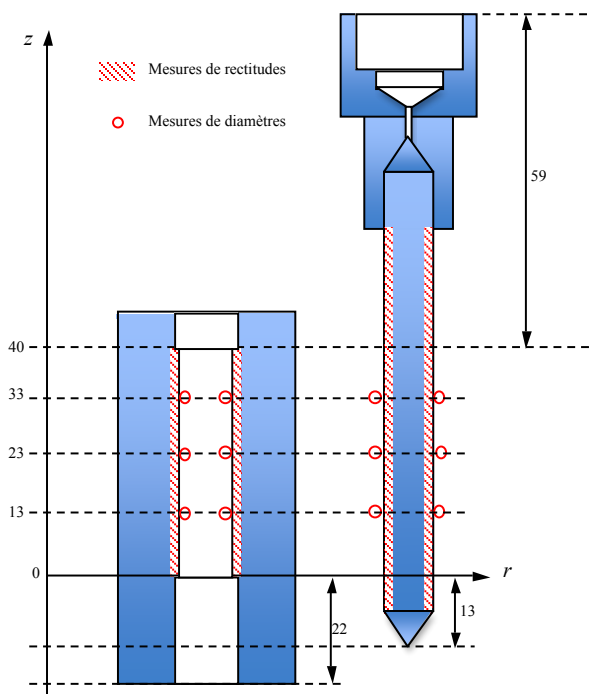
Position des mesures dimensionnelles du diamètre (en mm) et de la rectitude du piston et du cylindre, sur l'ensemble piston-cylindre 200 MPa N°4
